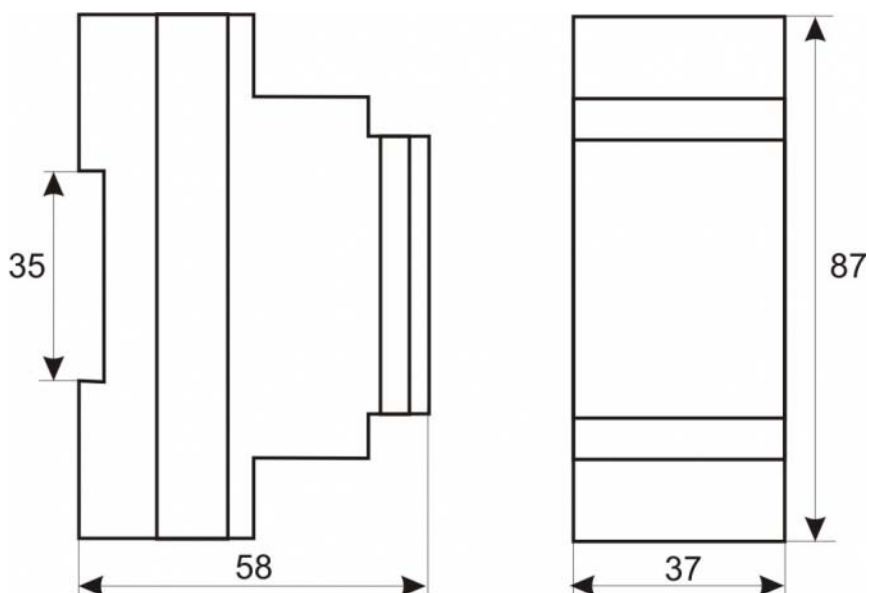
Габаритные размеры и внешний вид устройства УЗИП-III-2-DIN
